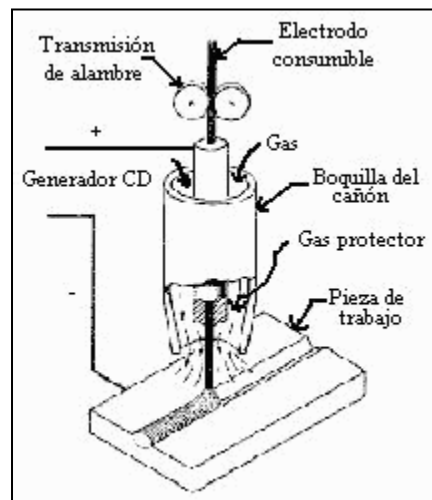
Soldadura GMAW. (Casioepa, 2010)
